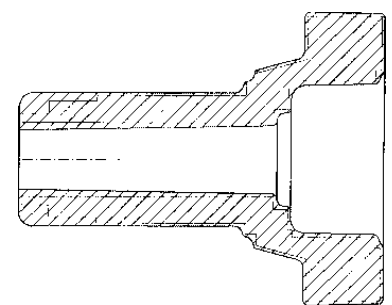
Варіанти виготовлення заготовок корпусу шліцевого
